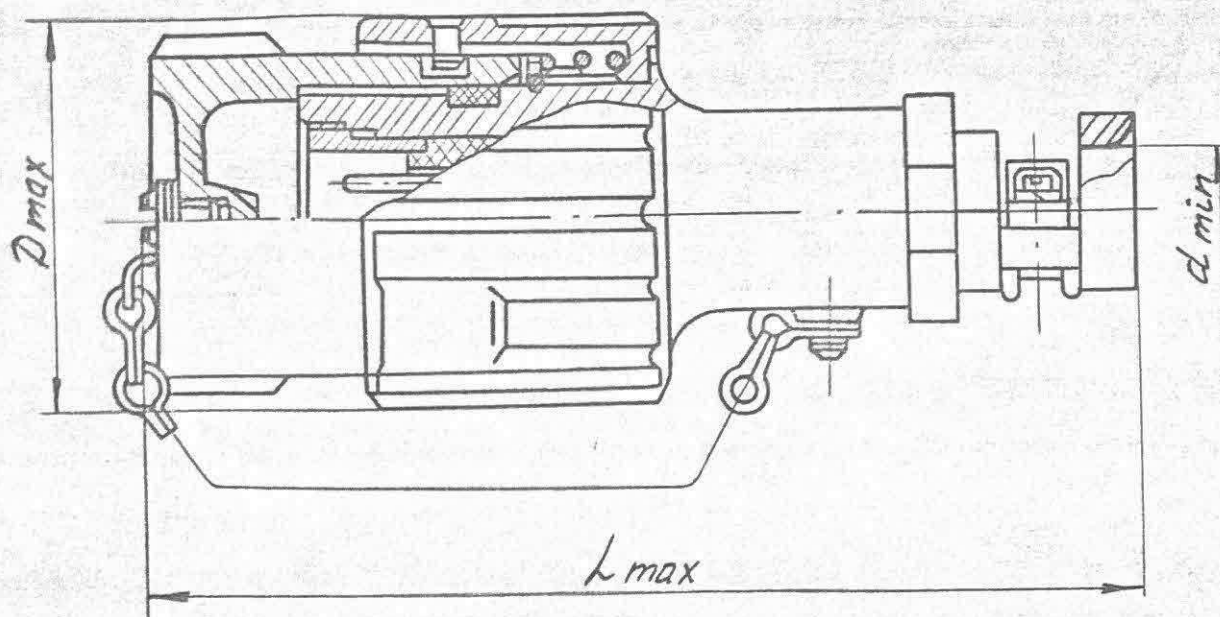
Вилка кабельная в прямом корпусе.
